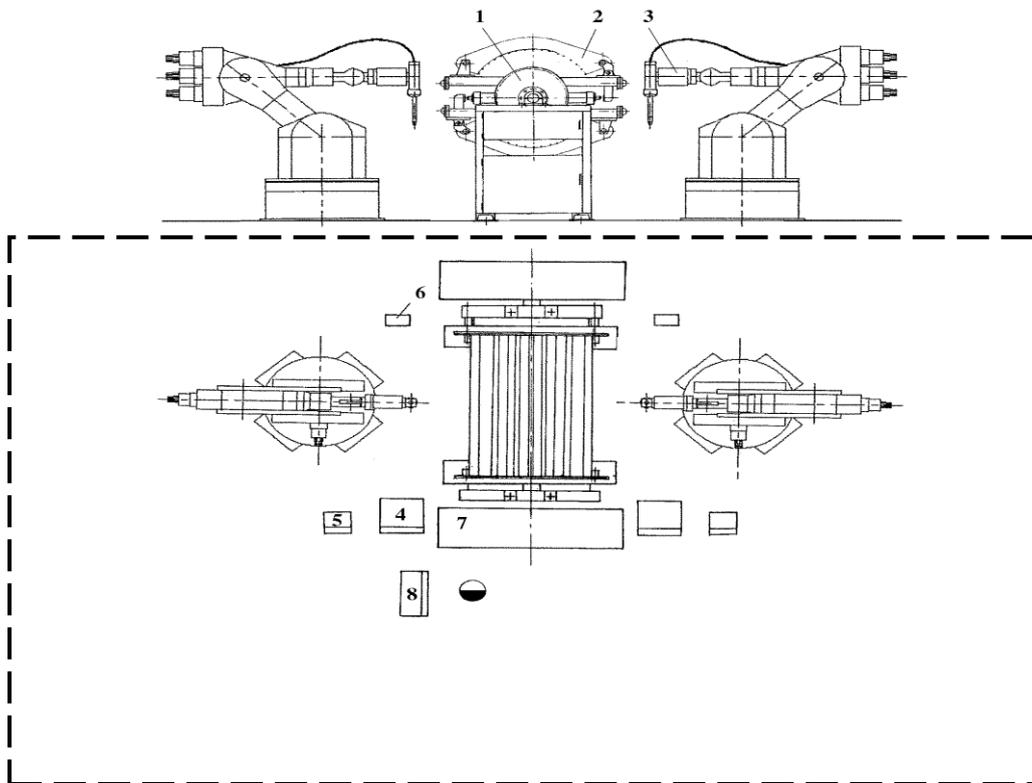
Схема роботизированного комплекса сварки каркаса
